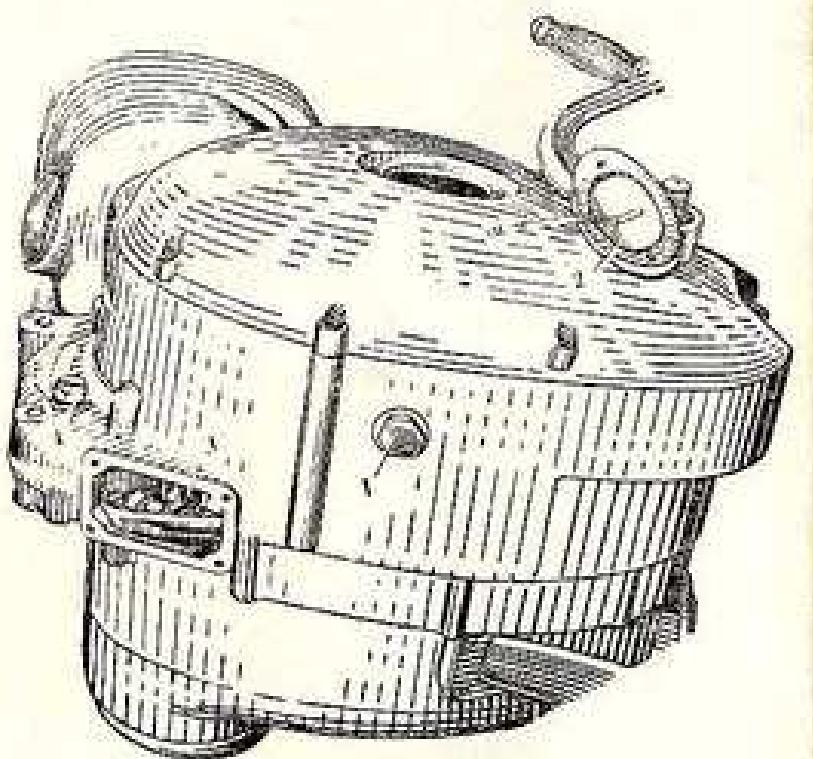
ВИД ДВИГАТЕЛЯ СНИЗУ:
